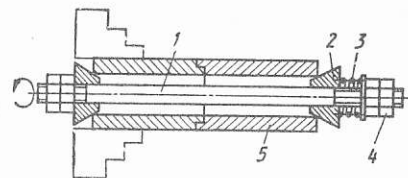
Приспособление для электронно-лучевой сварки
